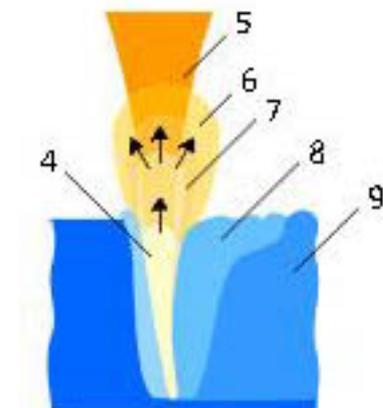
Laserstrahl-tiefschweißen
